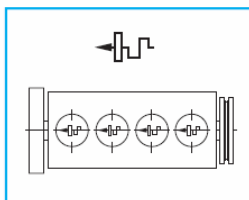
в. Расшифровка маркировки поршня из каталога фирмы Kolbenschmidt [2].
